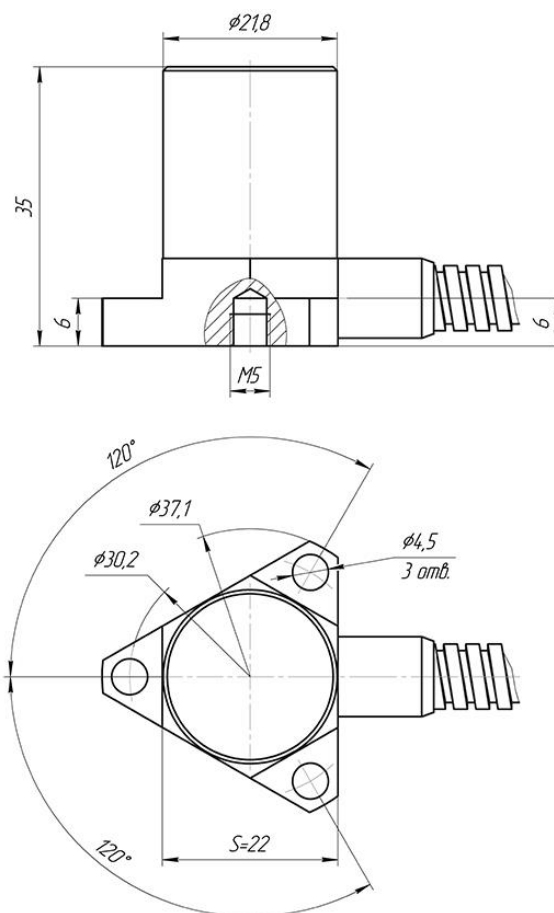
Габаритный чертеж велосиметра ZET 114
